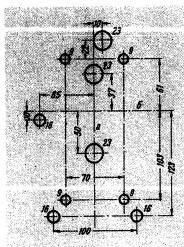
Сверление отверстий для установки на изоляционных панелях контакторов типа КП 523 и КП 533 с задним присоединением
